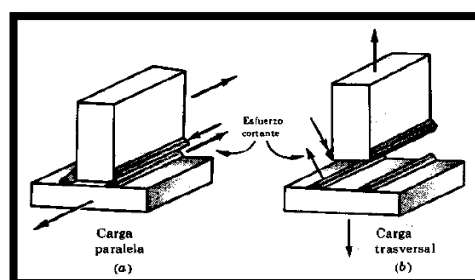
Tipos de Cargas que soporta el filete de soldadura (A.S.Hall).
